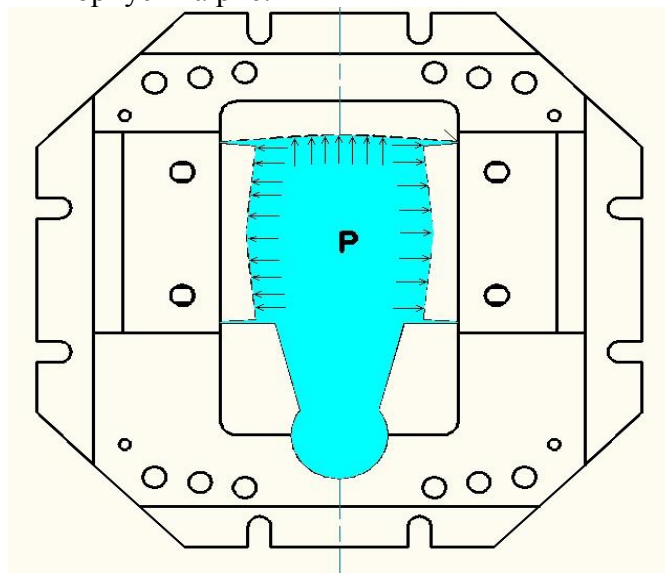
Влияние давления на формообразующие вставки пресс-формы. Где а-вид на подвижную полуформу; P-давление металла; 1-возможный прогиб формообразующих вставок и обоймы.
